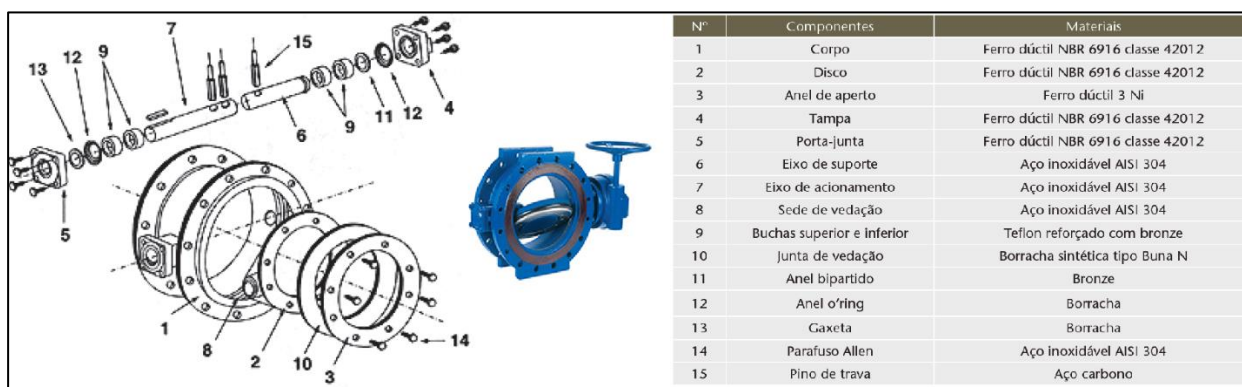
Exemplo ilustrativo de uma válvula borboleta flangeada.
